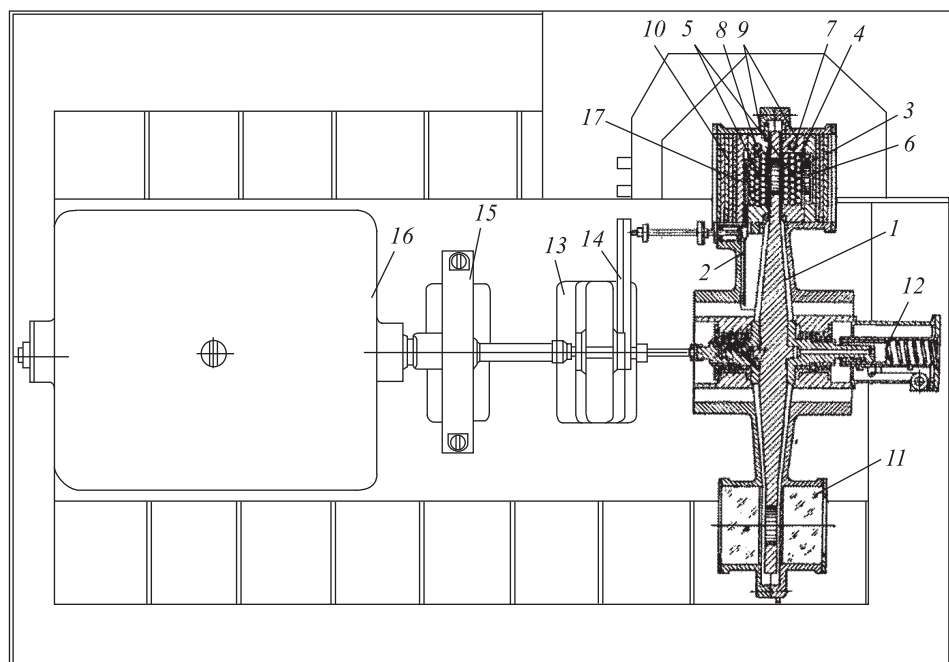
Конструктивная схема реактора ИБР: 1 — вращающийся диск; 2 — вспомогательный диск; 3 — основной вкладыш; 4 — плутониевые стержни; 5 — аварийные стержни; 6 — грубый регулятор; 7 — стержень автоматического регулятора; 8 — стержень ручного регулятора; 9 — боковой отражатель; 10 — торцовый отражатель; 11 — защитное стекло; 12 — механизм для установки основного вкладыша в защиту; 13 — ускоритель; 14 — редуктор вспомогательного вкладыша; 15 — тормоз; 16 — электропривод; 17 — вспомогательный вкладыш
